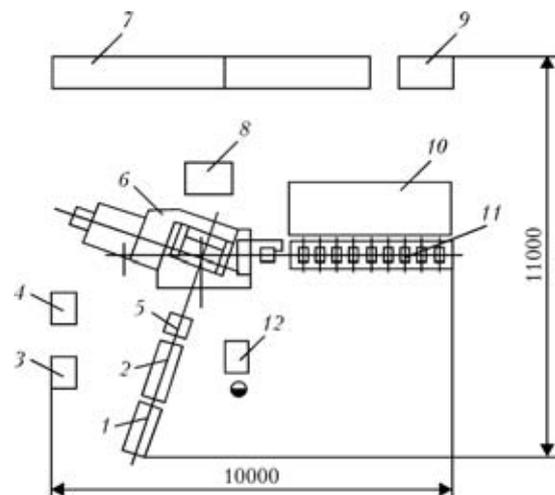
Схема линии для производства спиральношовных труб: 1 — разматыватель; 2 — подающая машина; 3 — шкаф управления линии; 4 — шкаф управления плазморезки; 5 — стыковочное устройство; 6 — формовочно-сварочное устройство; 7 — генератор сварочный; 8 — сварочная головка; 9 — теплообменник; 10 — накопитель; 11 — приемный ролик с отрезным устройством; 12 — пульт управления
